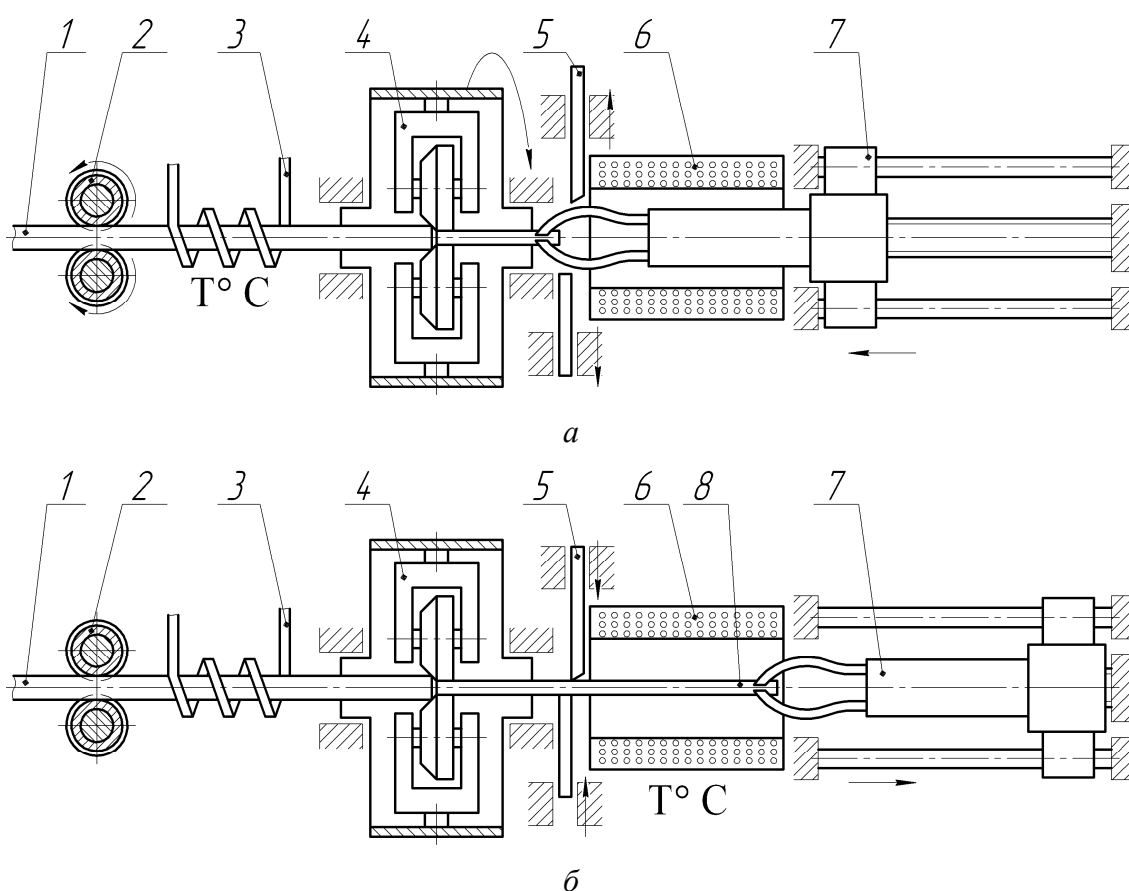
Установка для термомеханической обработки элинварных сплавов
